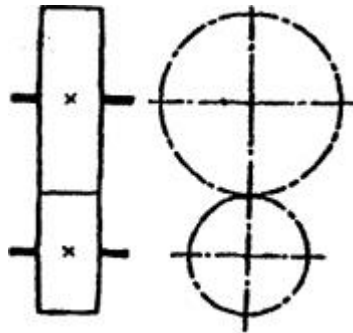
Условное обозначение зубчатой цилиндрической передачи с наружным зацеплением (показываются только делительные окружности)
